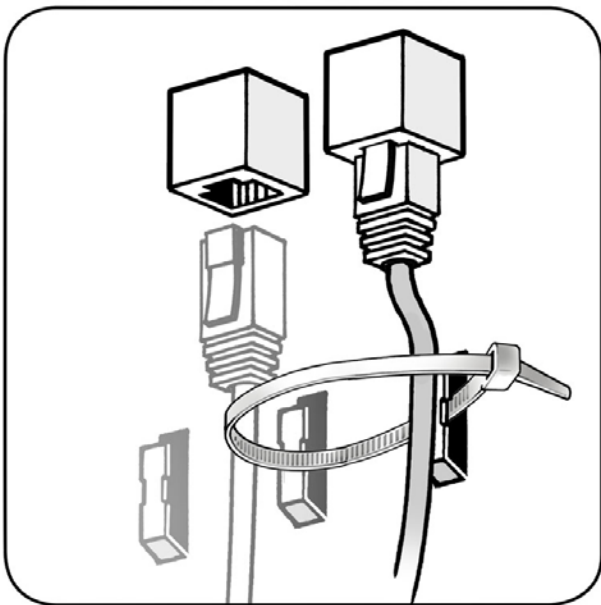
Befestigung der Kabel mit Kabelbindern
